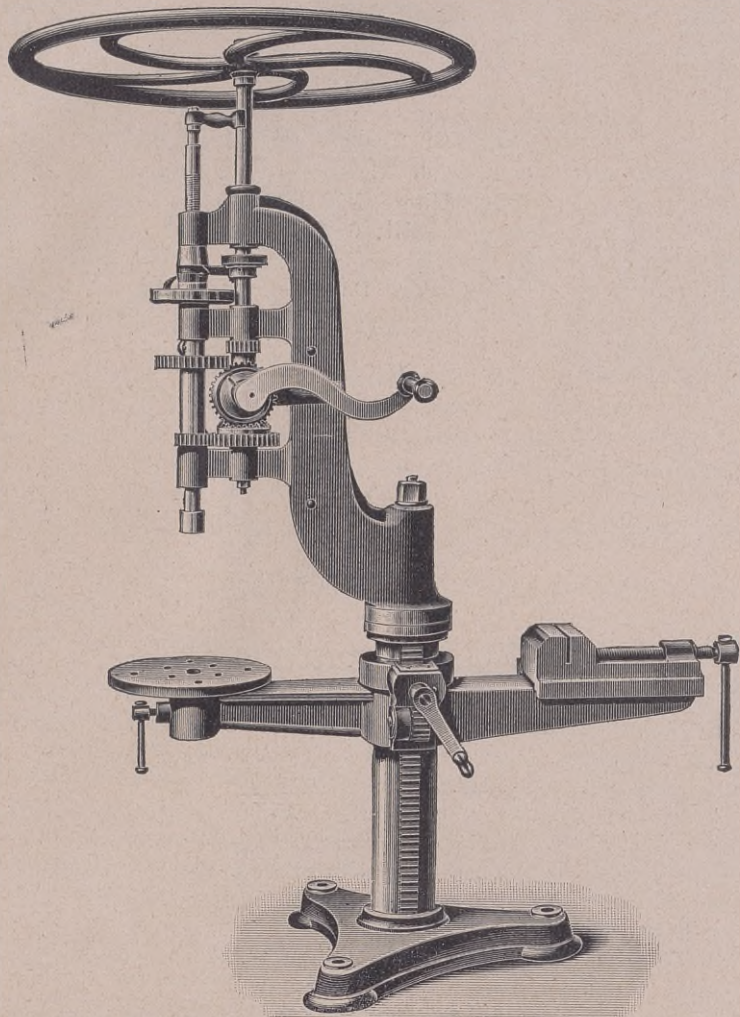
Säulenbohrmaschine für Handbetrieb.
